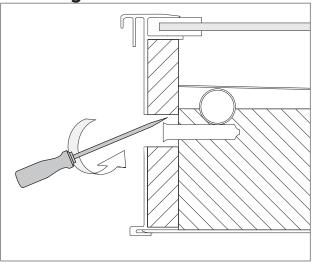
Gummistopfen aus Rahmen entfernen. Mit Schraubendreher eventuell Fühlerhülse freilegen.
